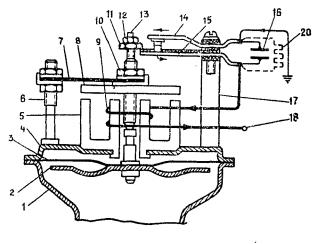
Схема электрического вибрационного сигнала: I— рупор: 2— вибрационный диск; 3— мембрана; 4— корпус; 5— сердечник; 6— шпилька; 7— с: альная упругая пластина; 8— якорек; 9— обмотка; 10— гайка; 11— регулировочная гайка; 12— контргайка; 13— шток; 14— неподвижная пластника; 15— упругая пластника; 16— конденсатор; 17— кронштейн; 18— зажимы; 19— кнопка; 20— пскрогасящее сопротивление.
